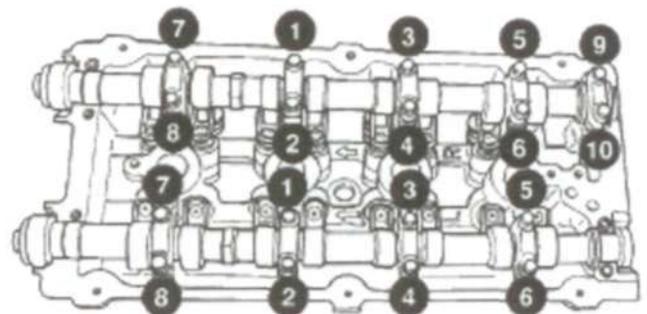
Последовательность затяжки крышки подшипника распредвала
